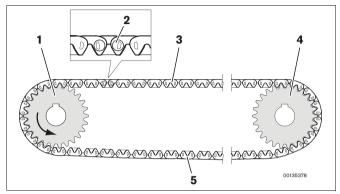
Цепной привод с транспортерной зубчатой цепью
